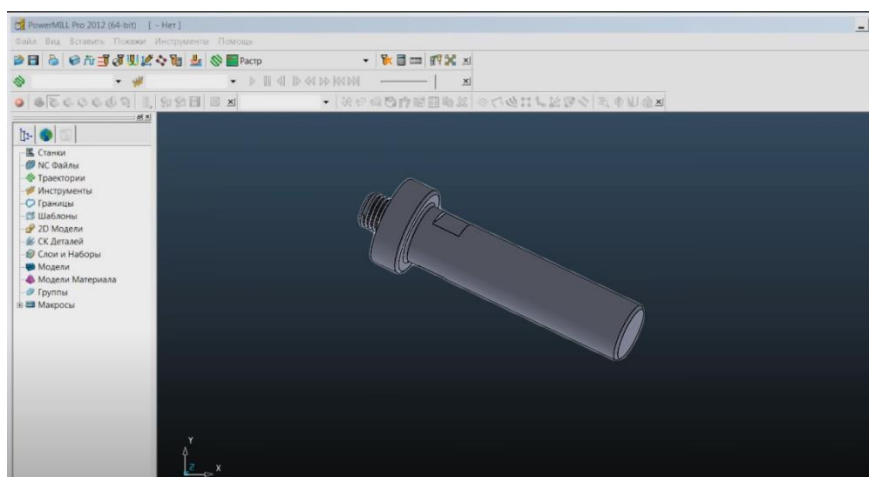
Модель деталі «Силовая скалка» у середовищі Power Mill
